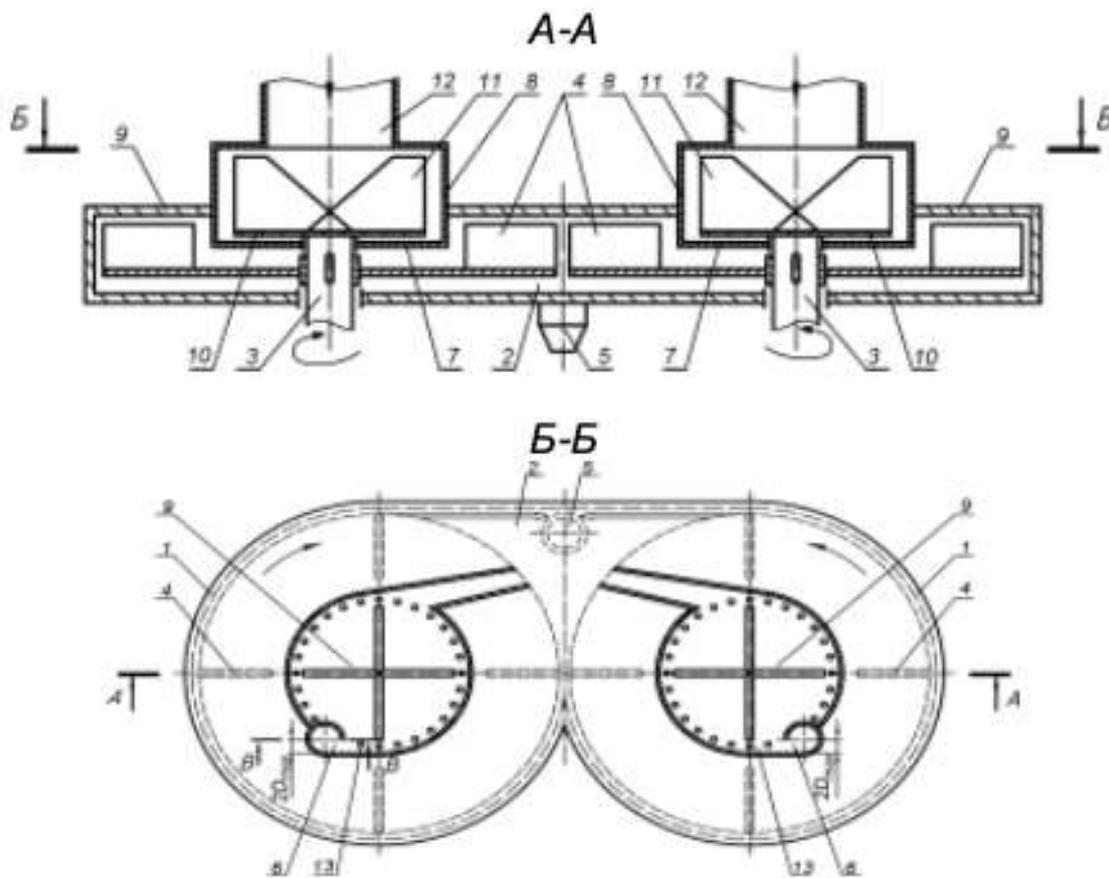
Центробежная мельница: 1 – корпус; 2 – тангенциальный канал; 3 – ротор; 4 – разгонные лопатки; 5 – выгрузочный патрубок; 6 – загрузочные патрубки; 7 – горизонтальная плита; 8 – верхняя ступень; 9 – нижняя ступень; 10 – верхний диск; 11 – разбрасывающие лопатки; 12 – загрузочный бункер; 13 – прутковая решетка; 14 – тангенциальный патрубок; 15 – тангенциальный отвод.
